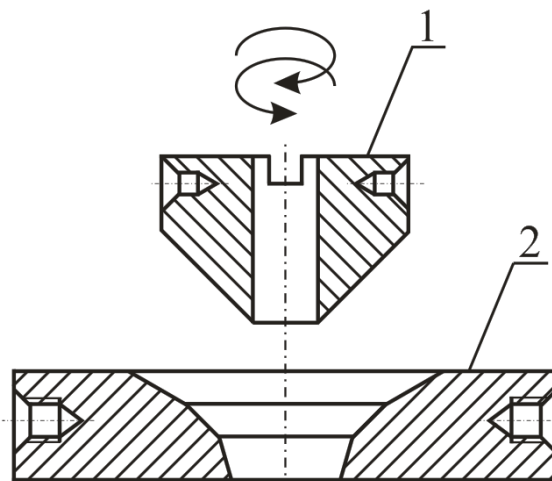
Схема розташування зразків [2]: 1 – зразок; 2 – контрзразок
